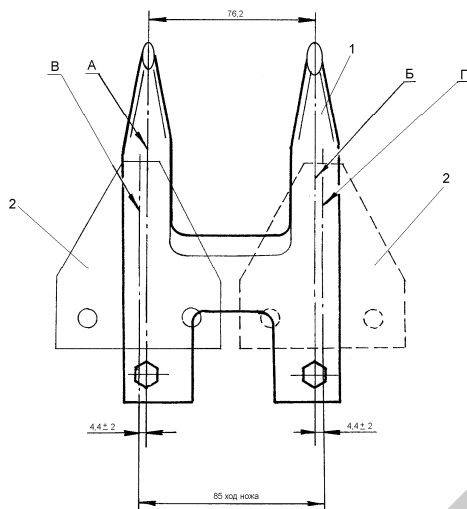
Регулировка перебега режущего аппарата жатки для зерновых культур:
